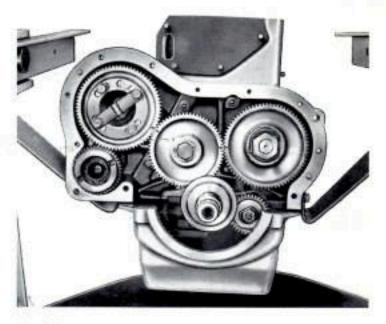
Smontaggio del motore: è stato tolto il coperchio ingranaggi distribuzione.
